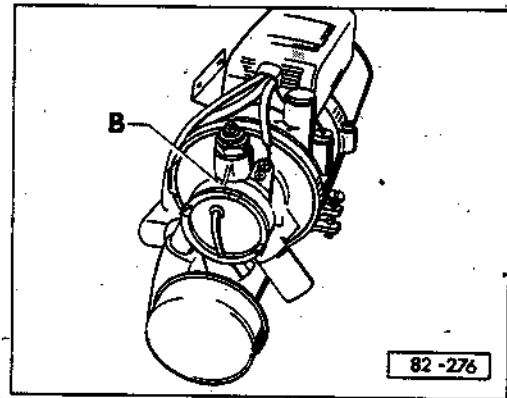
Vlies für Dieselheizgerät instand setzen
